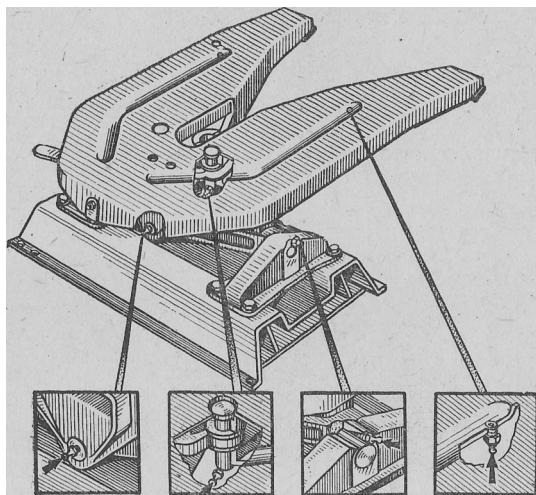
Карта смазки седельного устройства тягача ЗИЛ-181В
